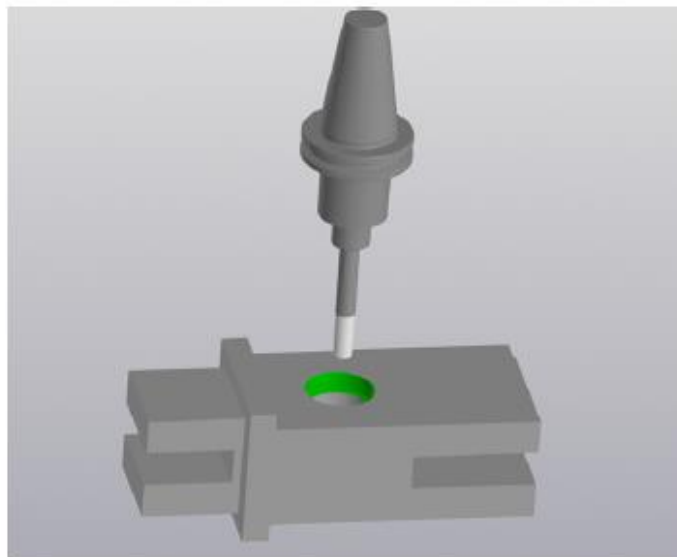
Модель операцій: 030.01 Фрезерування чорнове; 030.02 Фрезерування напівчистове; 030.03 Фрезерування чистове; 030.04 Фрезерування тонке. КОМПАС-3D v18.
